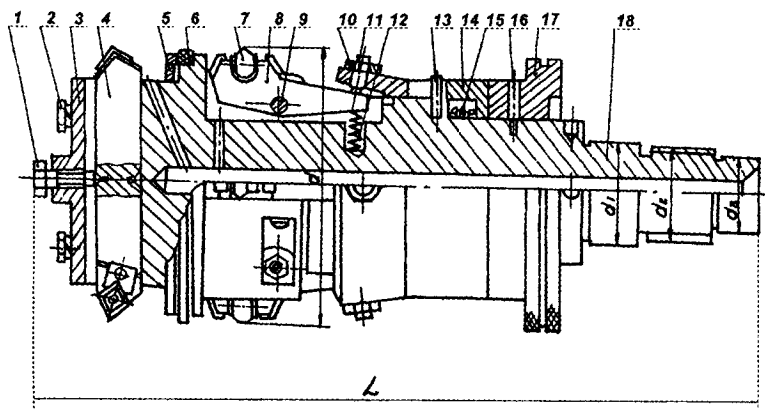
Комбінований інструмент для обробки різанням з ППД
